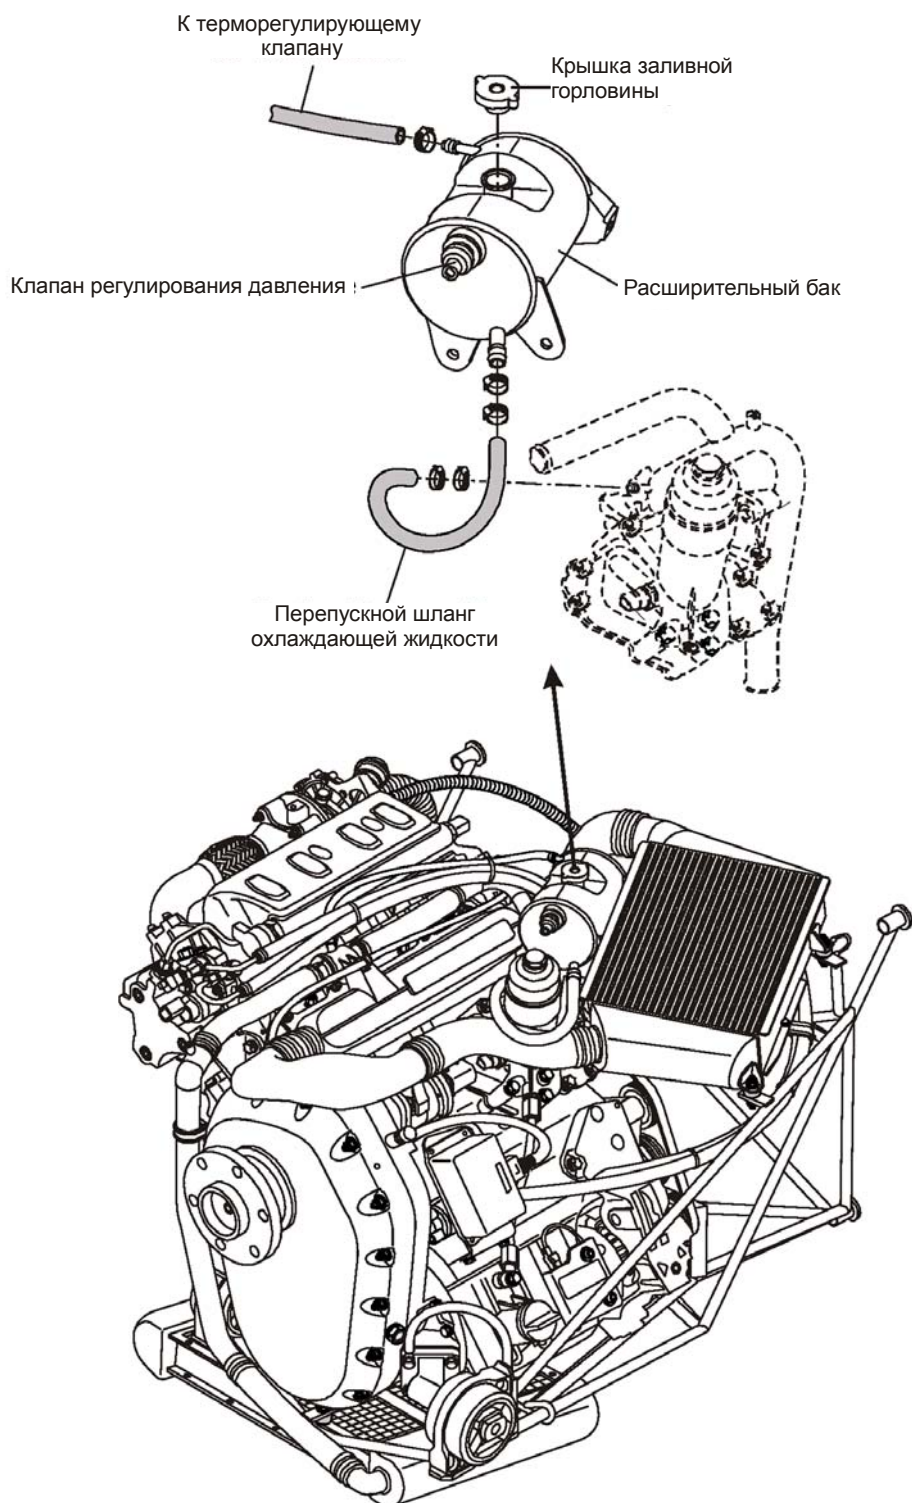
Расширительный бак охлаждающей жидкости двигателя и крышка заливной горловины
